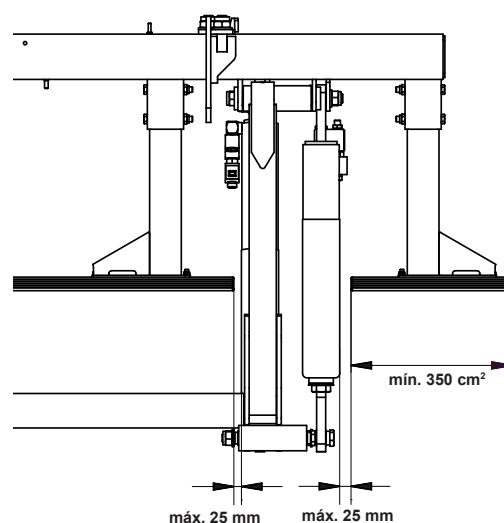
La distancia lateral entre la protección contra el empotramiento y las piezas móviles del elevador trasero
